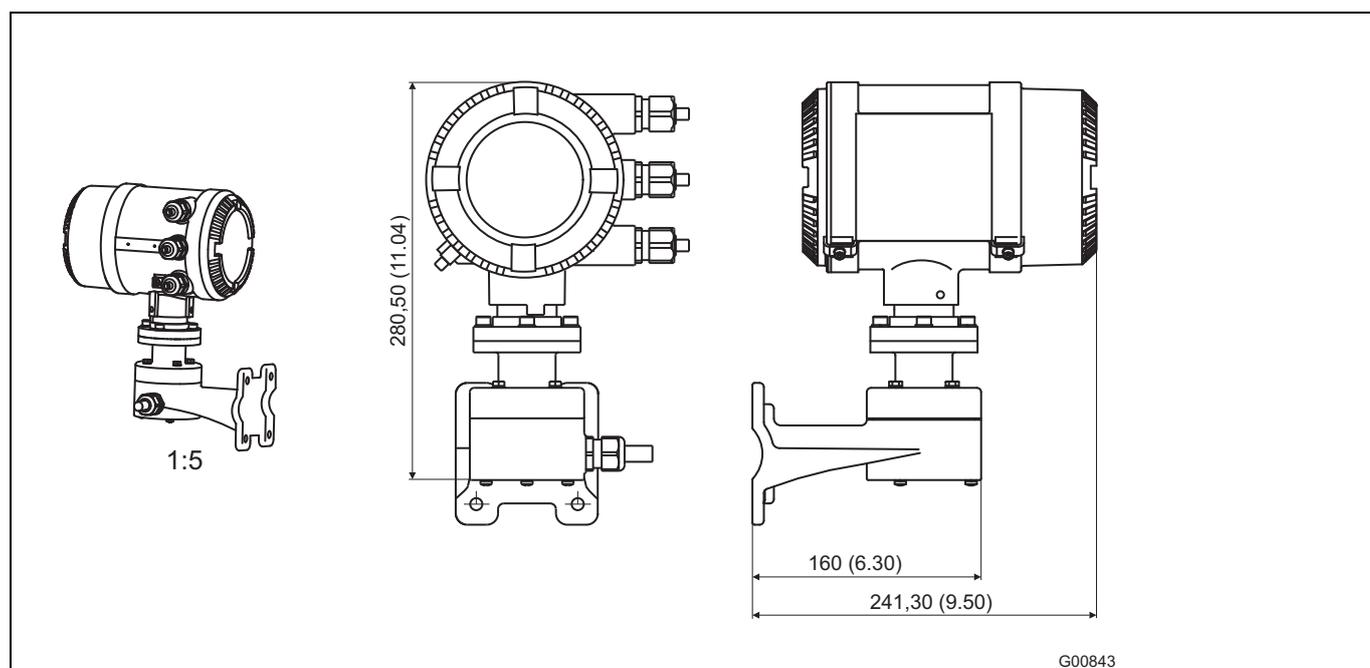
Габариты корпуса трансмиттера ME26/27/28
